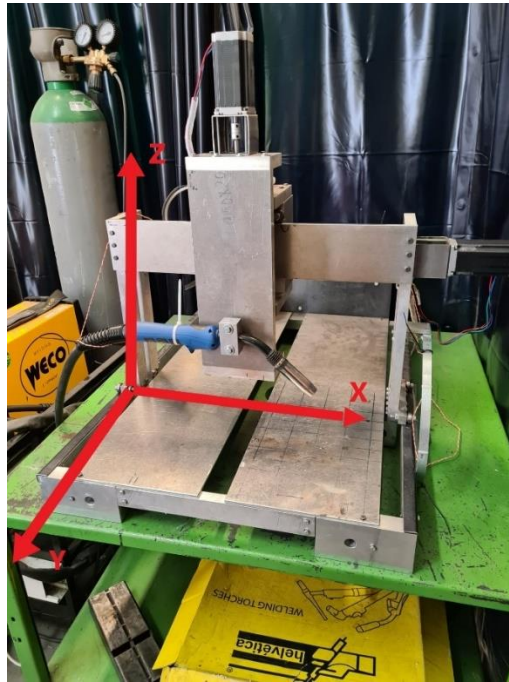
Mecanismo de soldadura utilizado para realização dos cordões de solda com seus respectivos eixos.
